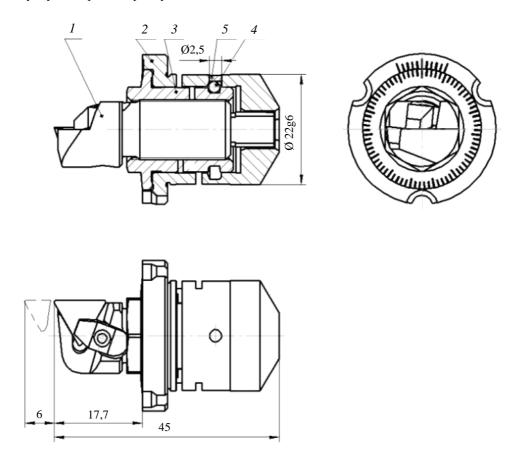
Резцовая вставка с креплением режущей пластины прихватом
